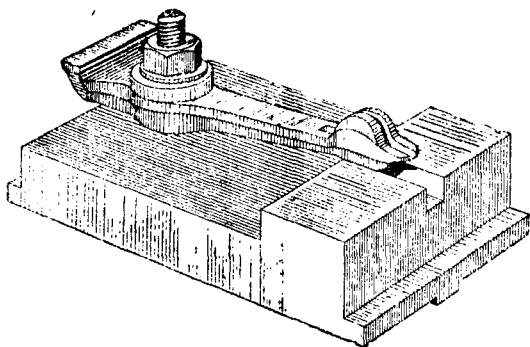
Приспособление для крепления губки ручных слесарных тисков при фрезеровании паза в шарнире.
